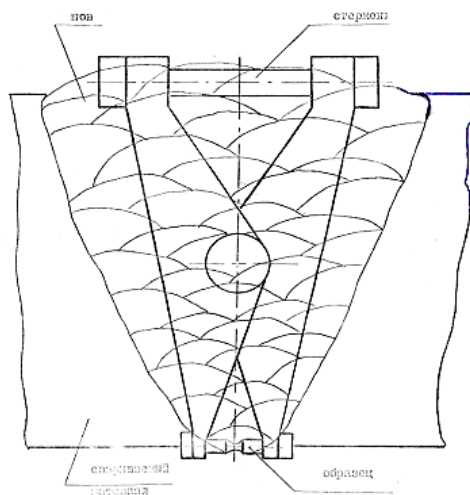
Схема имитации работы многопроходного сварного шва
